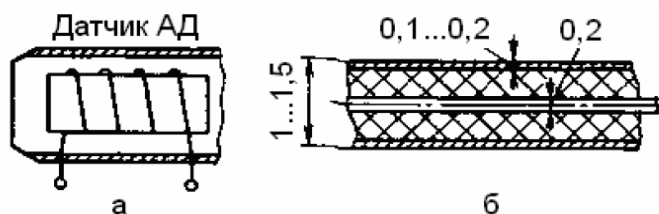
Линейный электротепловой ДПС: а - компоновка на корпусе двигателя; б – устройство датчика
